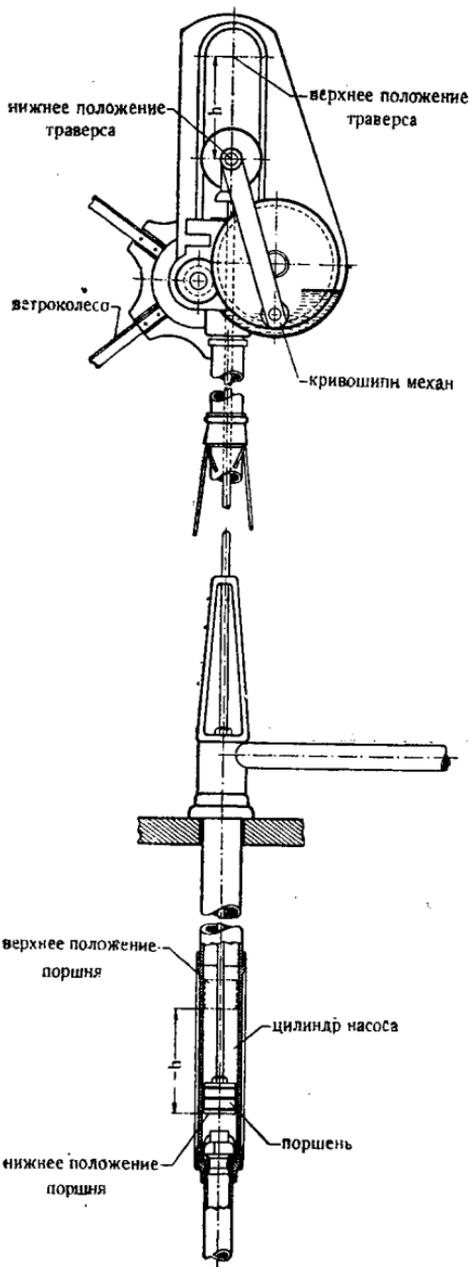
Конструкция рычагов для передачи движения от штанги ветродвигателя к штанге насоса
